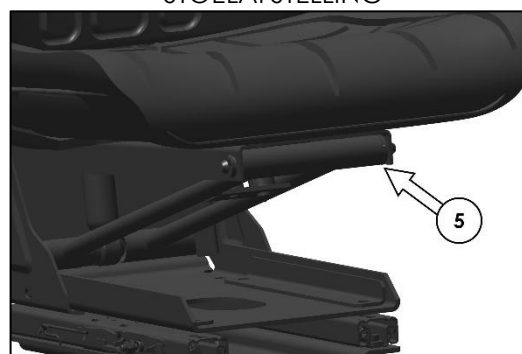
BEDIENINGSELEMENTEN VOOR STOELAFSTELLING
